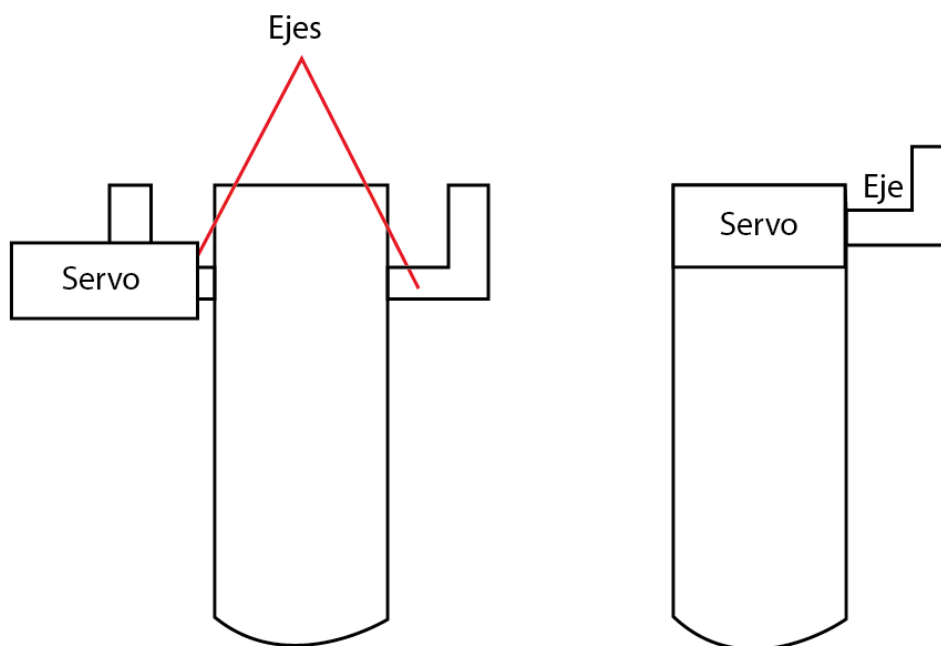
Diseño definitivo sistema cambio ejes; Fuente propia
